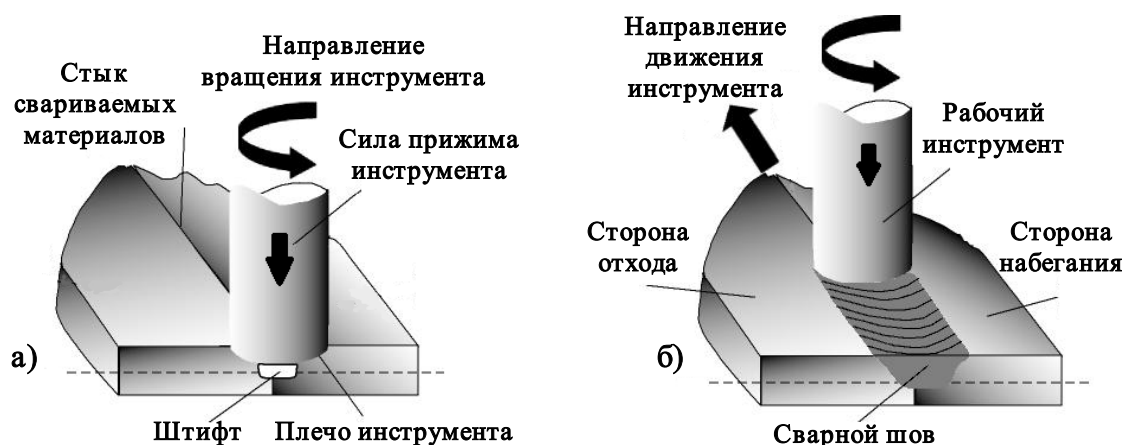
Схема процесса сварки трением с перемешиванием.
